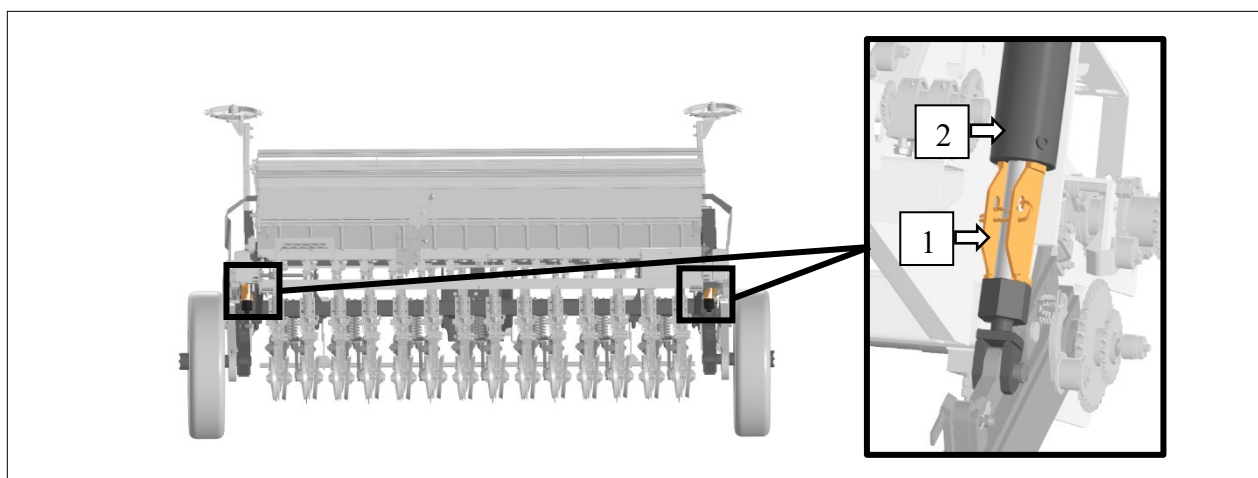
Транспортные упоры на штоках гидроцилиндров
